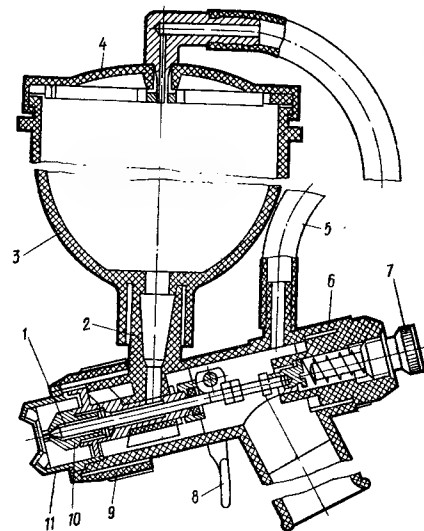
Краскораспылитель ручной пневматический низкого давления СО-44А:
